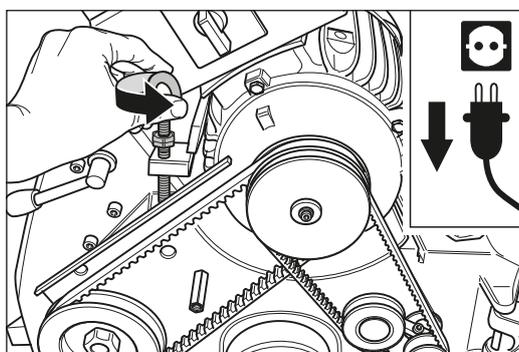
Destensado de las correas trapezoidales aflojando el cáncamo de elevación.
